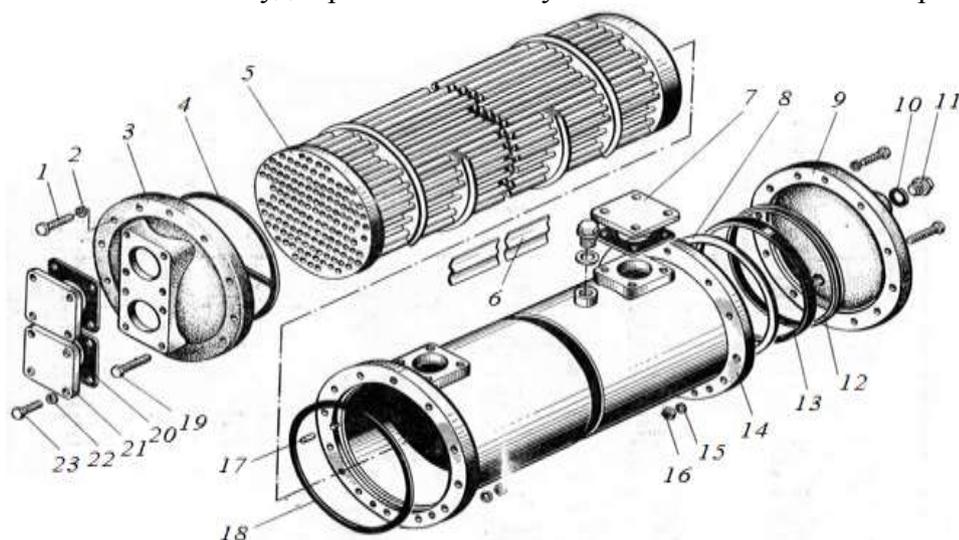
Водоподогреватель трубчатого типа, где: 1 – болт; 2 – гайка; 3 – передняя крышка; 4 – прокладка; 5 – пакет трубок; 6 – цинковый протектор; 7 – заглушка; 8 – проставочное кольцо; 9 – задняя крышка; 10 – уплотнительное кольцо; 11 – пробка; 12 – прижимное кольцо; 13 – сальниковое уплотнение; 14 – фланец; 15 – шайба; 16 – гайка; 17 – штифт; 18 – проставочное кольцо; 19 – болт; 20 – прокладка; 21 – заглушка; 22 – шайба; 23 – болт.
